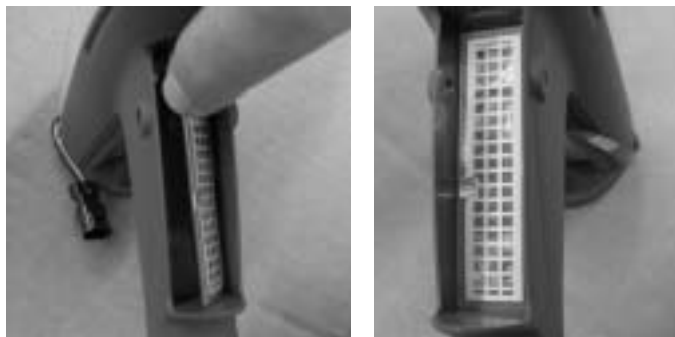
Installazione dell'interruttore dell'azionamento - Punto 4
